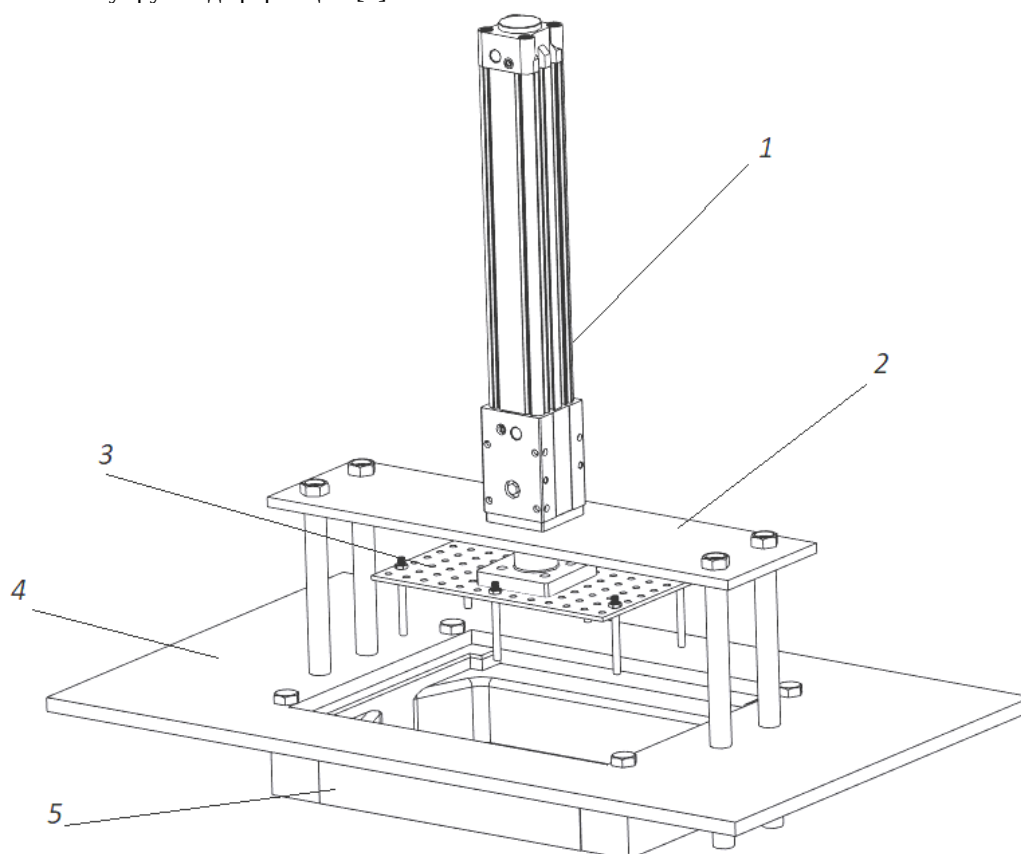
Пневматическое устройство для формования упаковочных лотков
